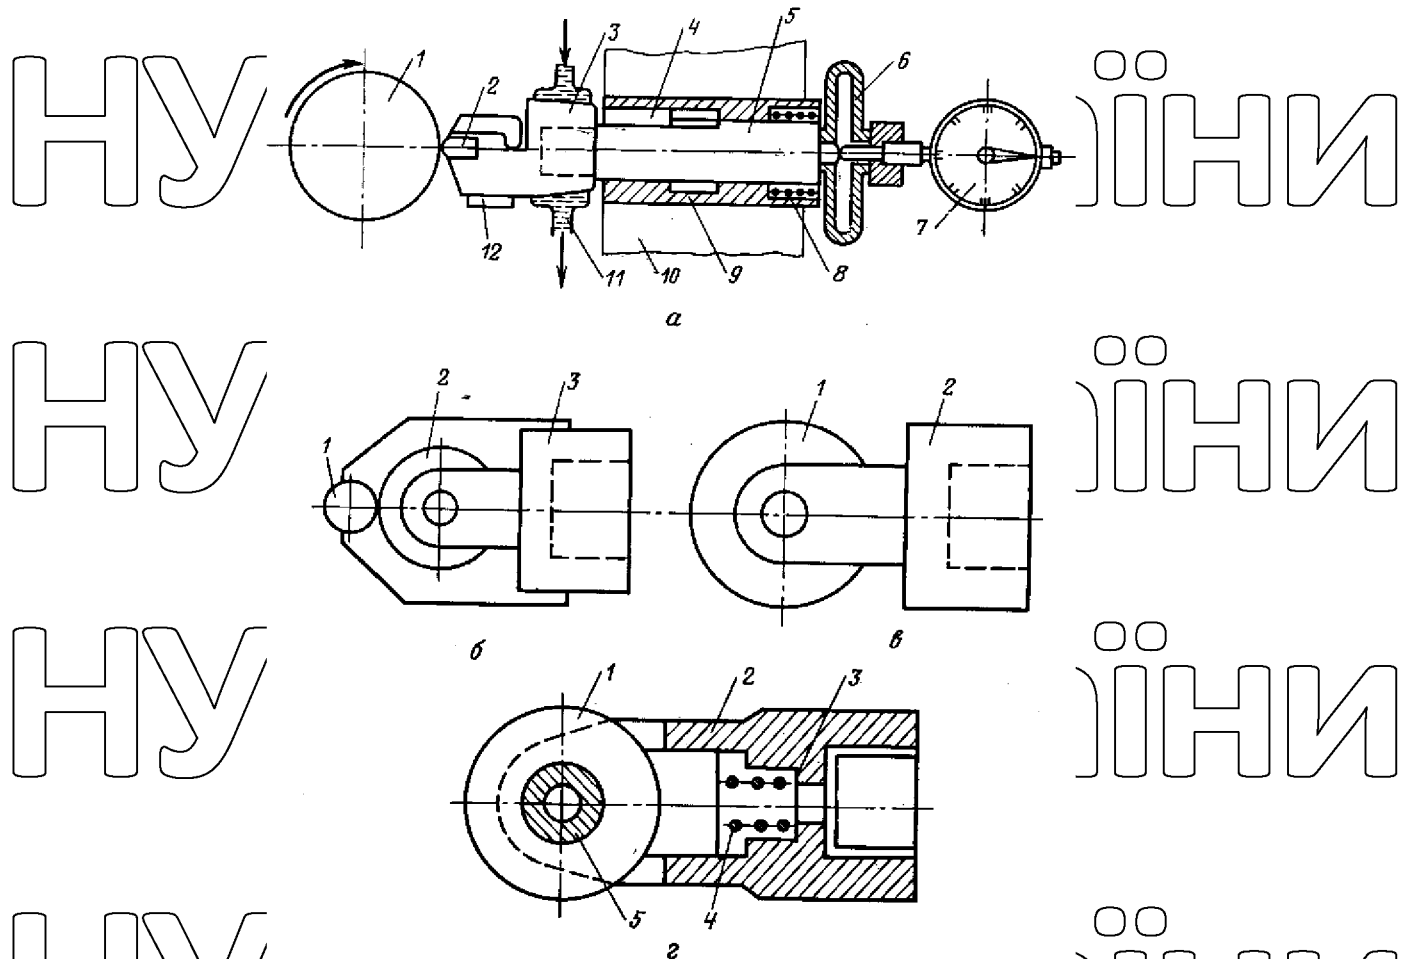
Схема динамометричної оправки (а) зі змінними головками (б, в і г) для зміцнення ЕМО та ППД деталей, відновлених металопокриттями: а - оправлення: 1-деталь; 2 - інструмент; 3 - головка для інструменту; 4 - шпонка; 5 - шток; 6 пружний елемент; 7 -індикатор; 8 - пружина; 9 - втулка корпусу; 10 - супорт верстага; 11 - охолоджуючий кожух; 12 - наконечник струмопроводу, б - кулькова головка: 1 - кулька; 2 - кульковий підшипник; 3 - вилка головки; в і г - роликові головки: 1 - ролик; 2 -вилка головки; 3 - мідно-графітова щітка; 4 - пружина; 5-вісь ролика
